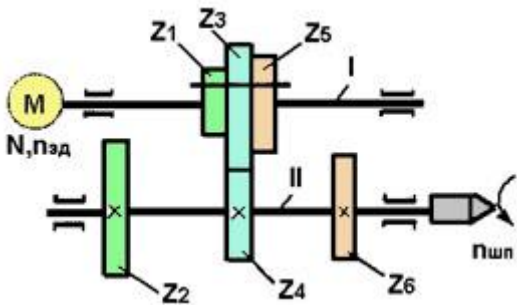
Регулирование с помощью передвижных блоков зубчатых колес.
